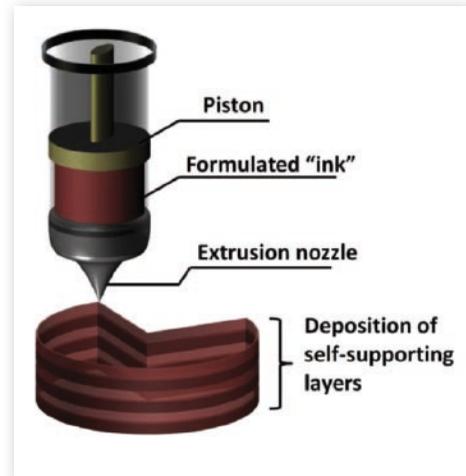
3D-Lebensmitteldruck auf Grundlage extrusionsbasierter Verfahren
